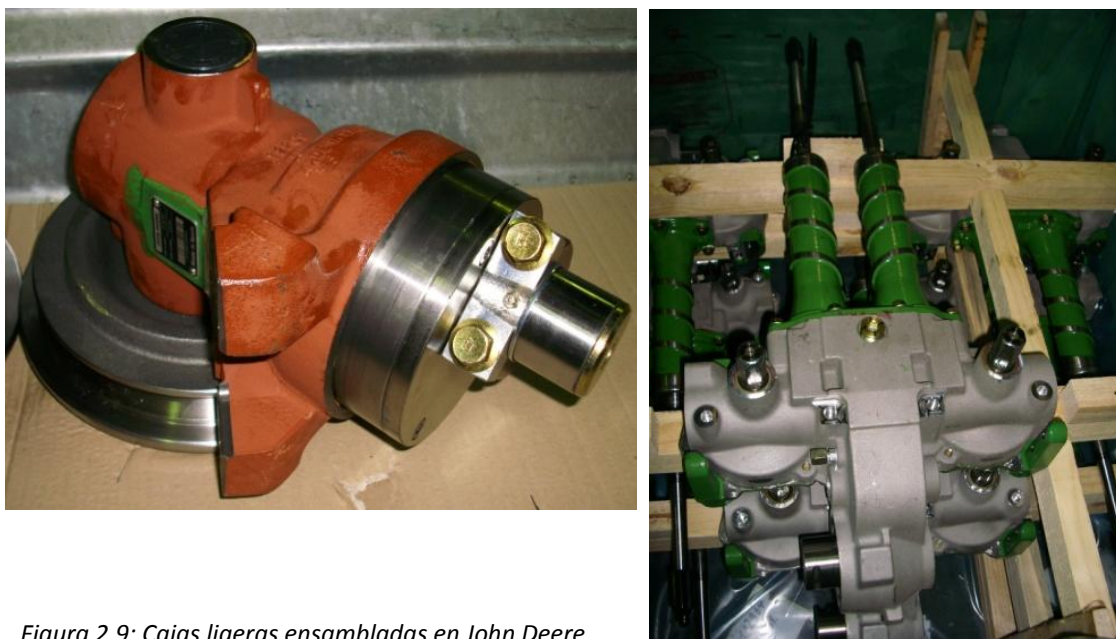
Cajas ligeras ensambladas en John Deere Ibérica.
